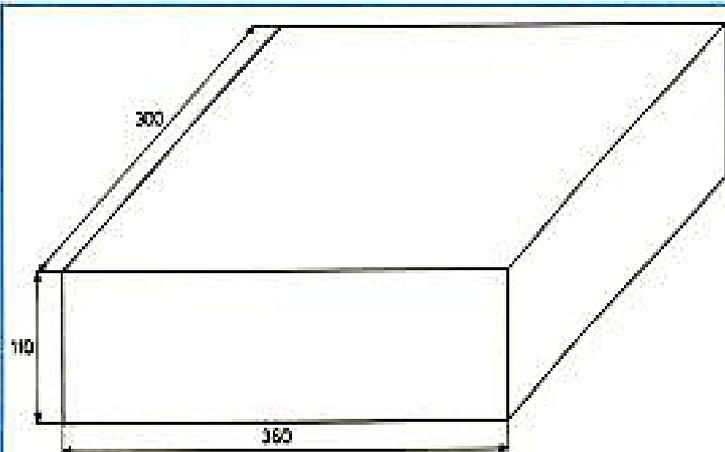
Dimensions du boîtier utilisé pour loger deux « drives ».
